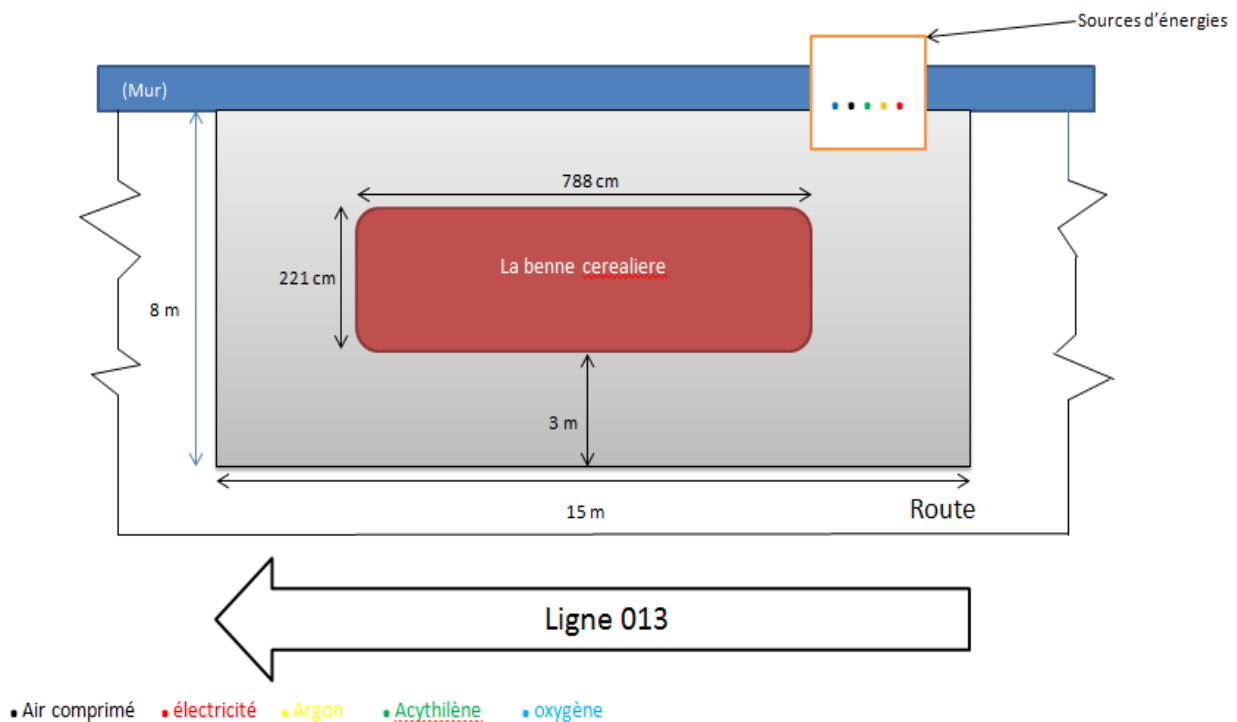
espace de travail soudage de la benne céréalière dans la ligne 013 hall 03
